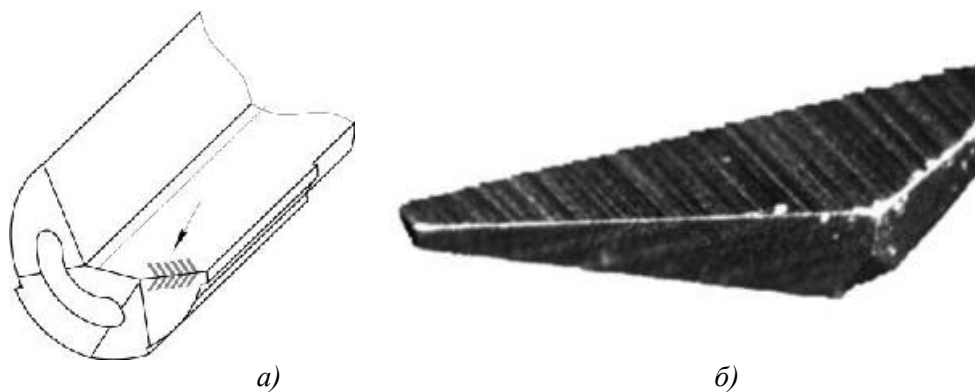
Схема режущей части ружейного сверла: а) - трёхмерная модель; б)- режущей кромки
